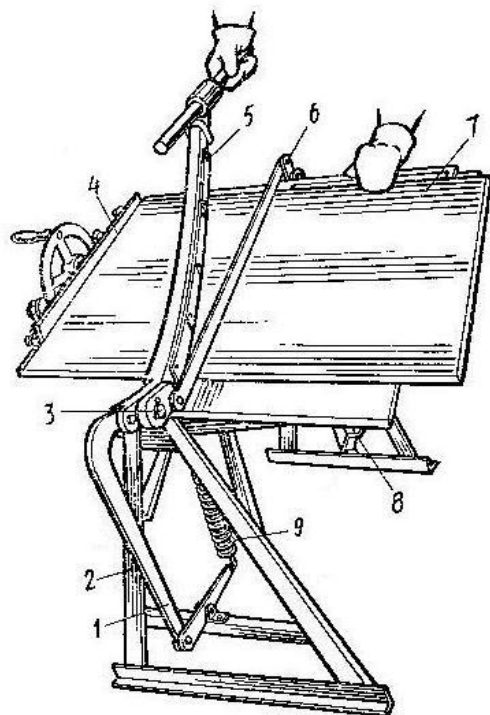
Резка металлического листа ручными маховыми (рычажными) ножницами:
